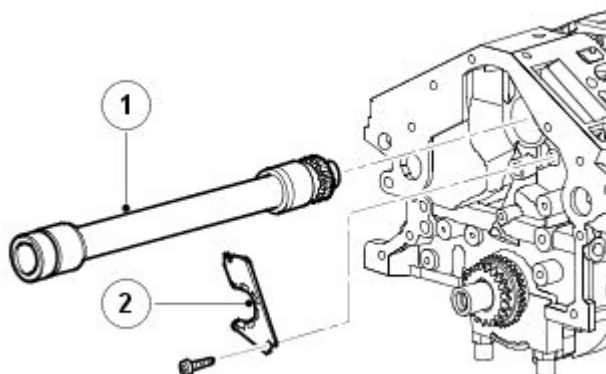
Промежуточный вал бензинового двигателя 4.0L V6
